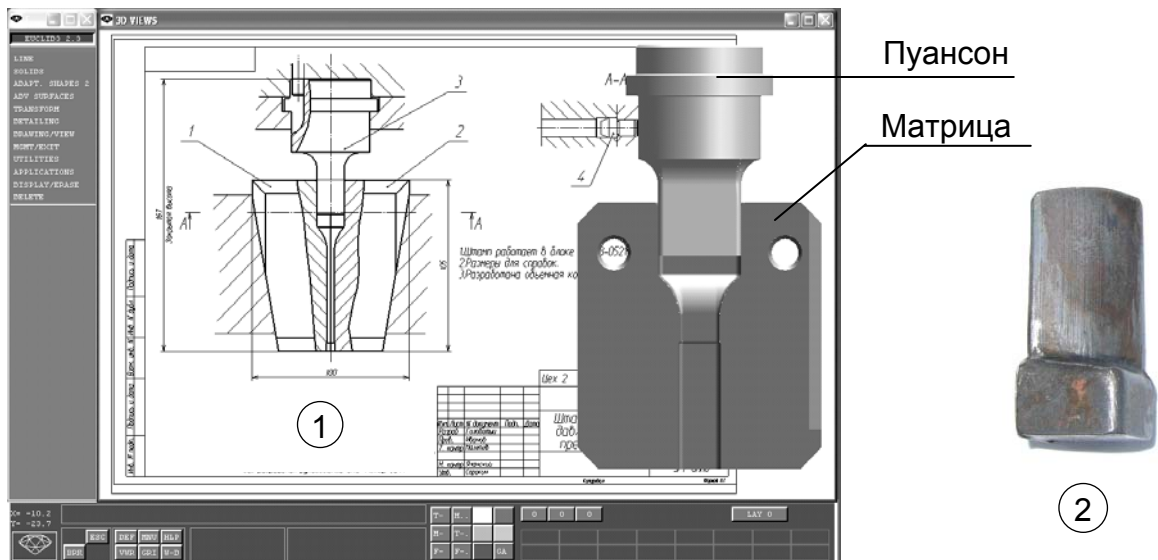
Экструдирование: 1 – аналитические эталоны формообразующих деталей и чертеж штампа для выдавливания; 2 – фото заготовки лопатки компрессора, полученной высокоскоростным выдавливанием.
